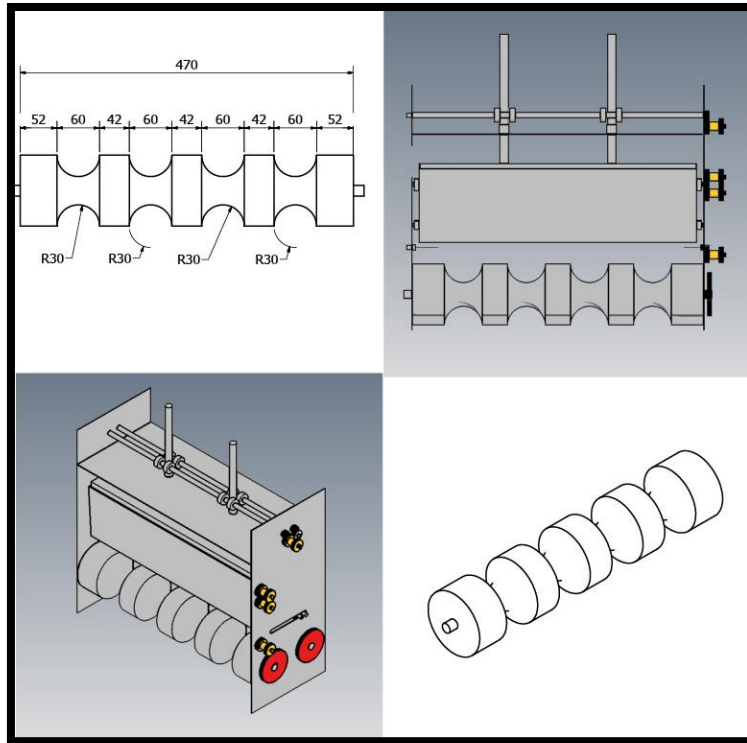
Hipótesis de sistema que combina la división por mecanismos de engranes y rodillos de boleó
